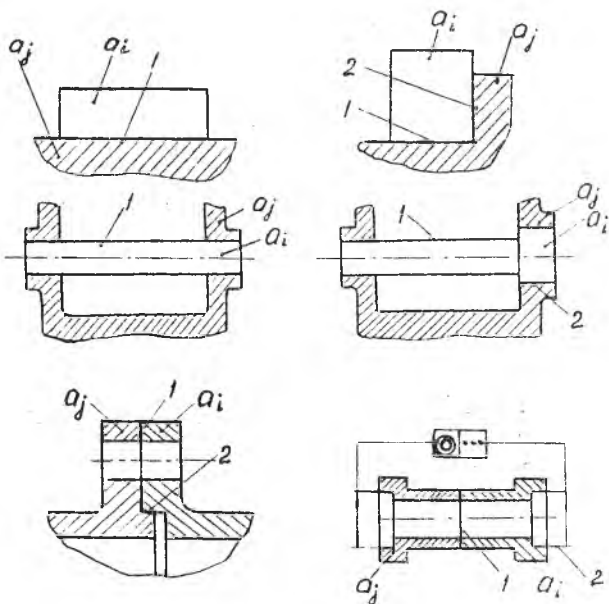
Примеры использования баз для деталей: a_i — базируемая деталь; a_j — базовая деталь; 1, 2 — базы
